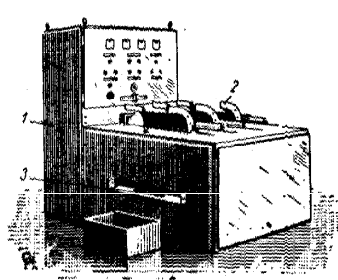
Нагреватель фирмы «Асек» для нагрева концов заготовок:
